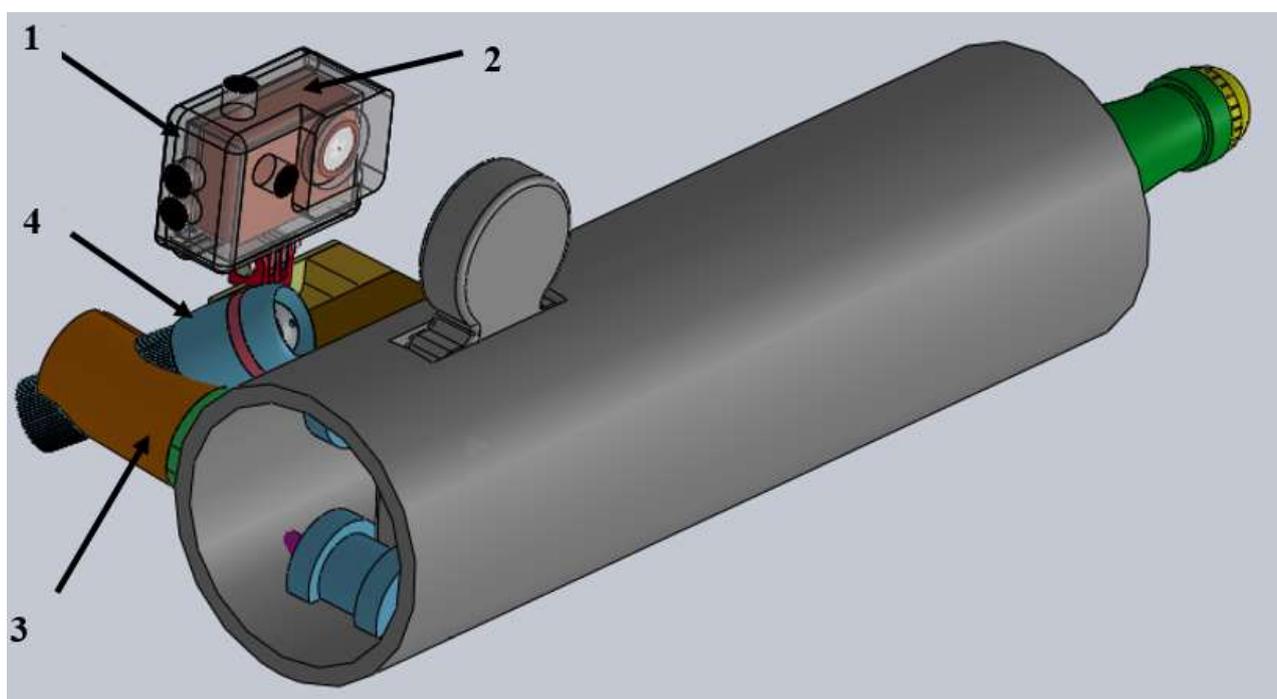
Стенд с системой фиксации измерений (1 – защитный бокс камеры, 2 – камера, держатель, 3 – фонарик)
